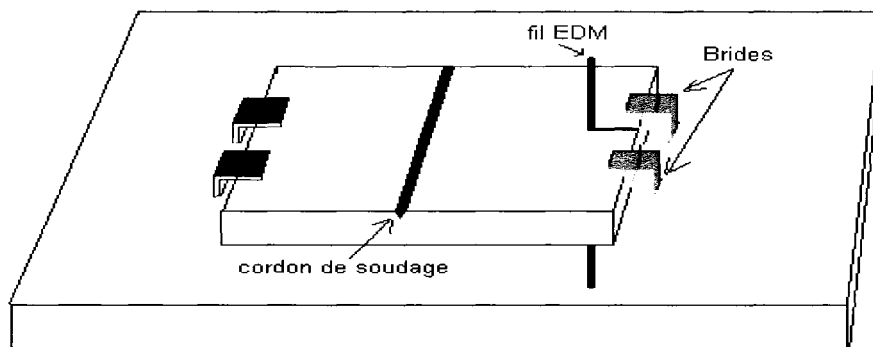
Ligne de coupe EDM sur la plaque soudée.
